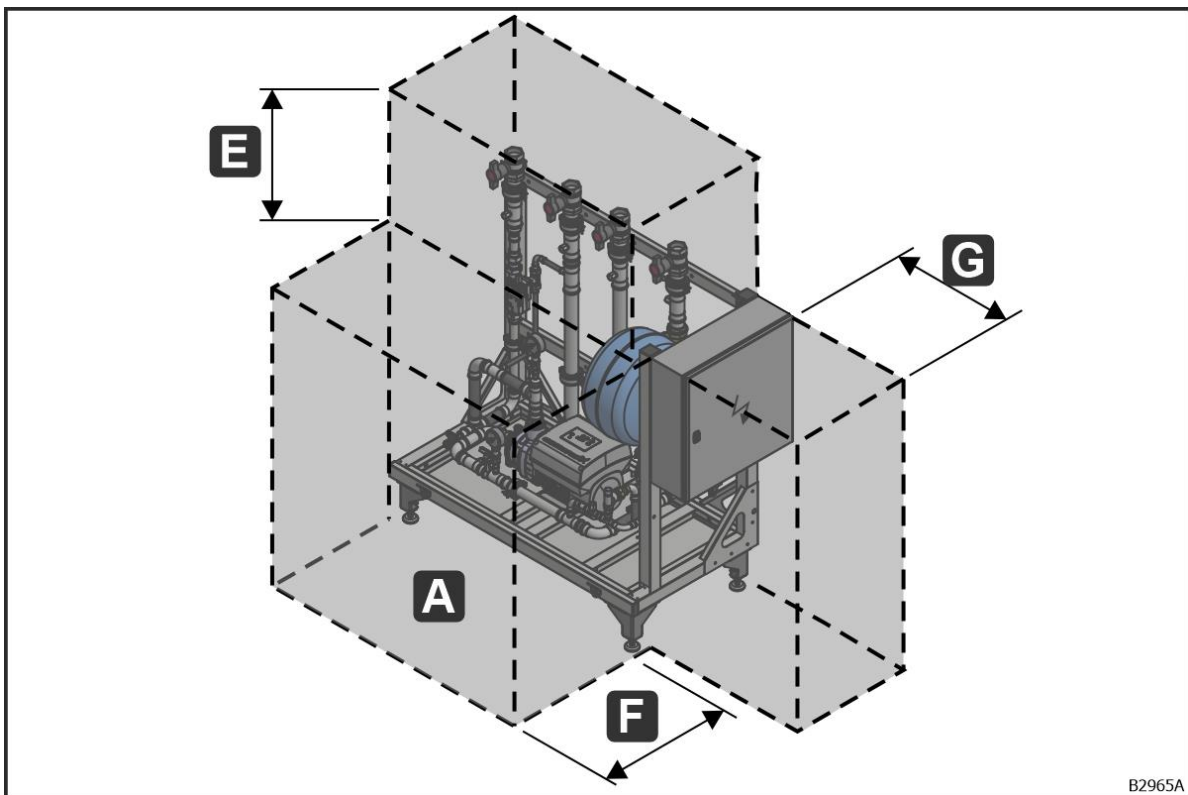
Encombrement du système hydraulique BEG HP sur pied
